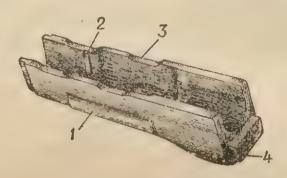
Цевье: 1 — упоры для пальцев; 2 — металлическая прокладка; 3 - вырезы; 4 - выступ
